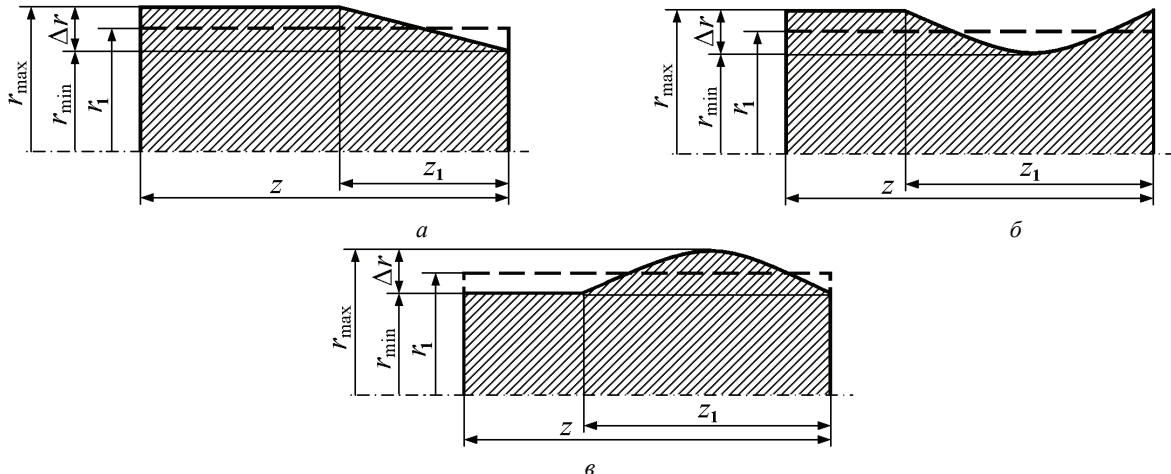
Модель досліджуваного вала: а – конусоподібний вал; б – сідлоподібний вал; в – діжкоподібний вал; z – довжина втулки (вала); z_1 – довжина геометричної аномалії; — — — вал правильної геометричної форми
